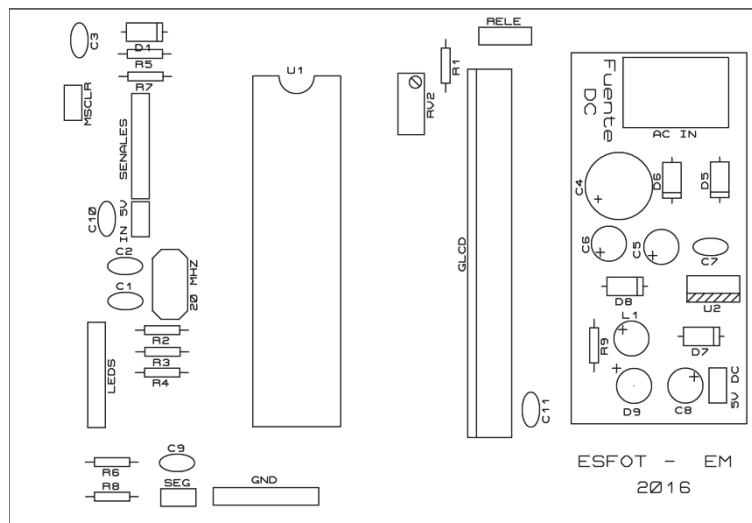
PCB de la tarjeta principal, contiene el PIC18F4550.
